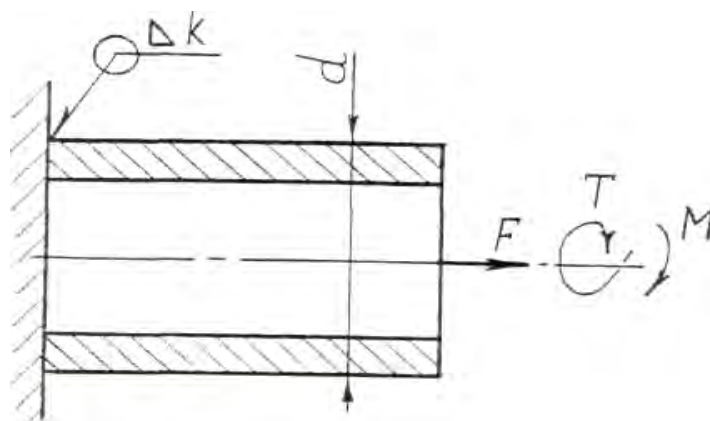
Соединение трубы с плитой методом сварки
